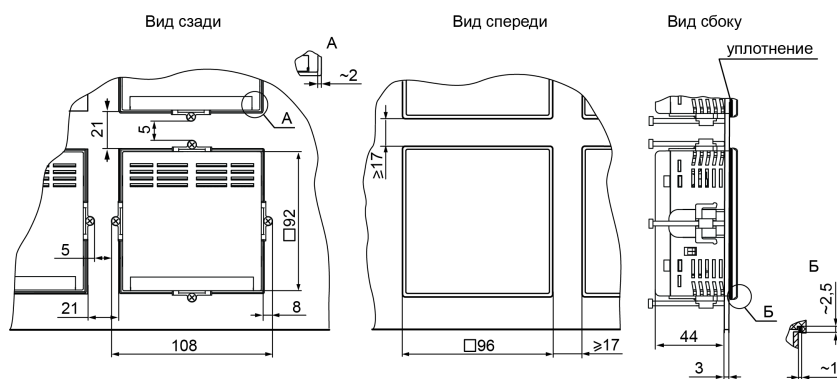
Прибор в корпусе Щ1, установленный в щит толщиной 3 мм
